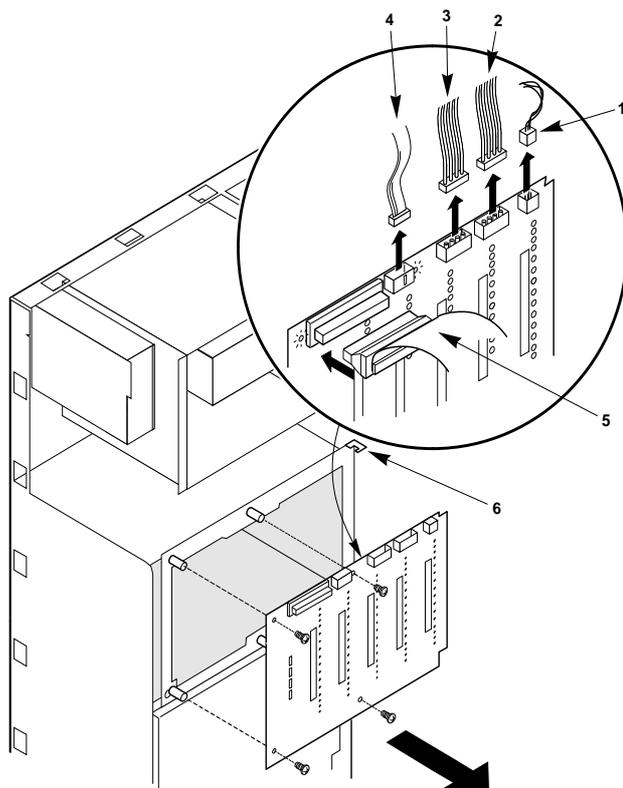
Entfernen einer Hot-docking Rückwand
